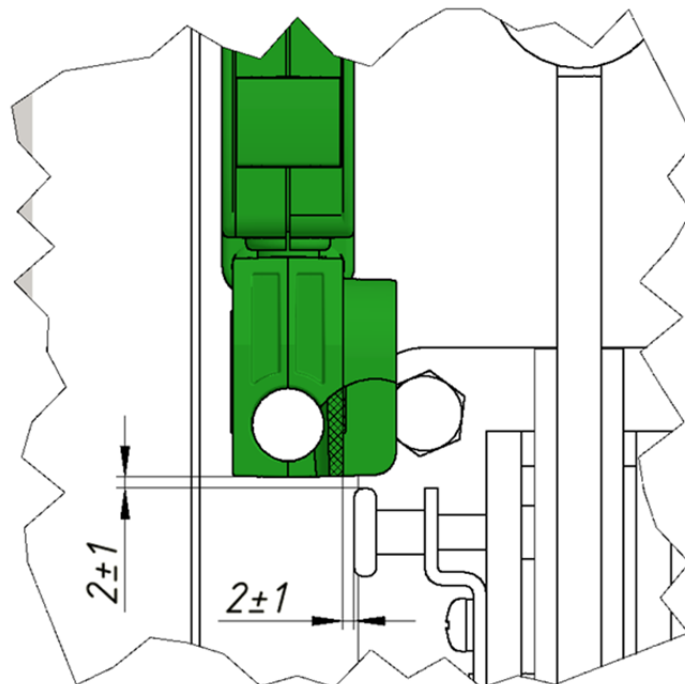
Установка блокиратора с разнесенными разъединителями
